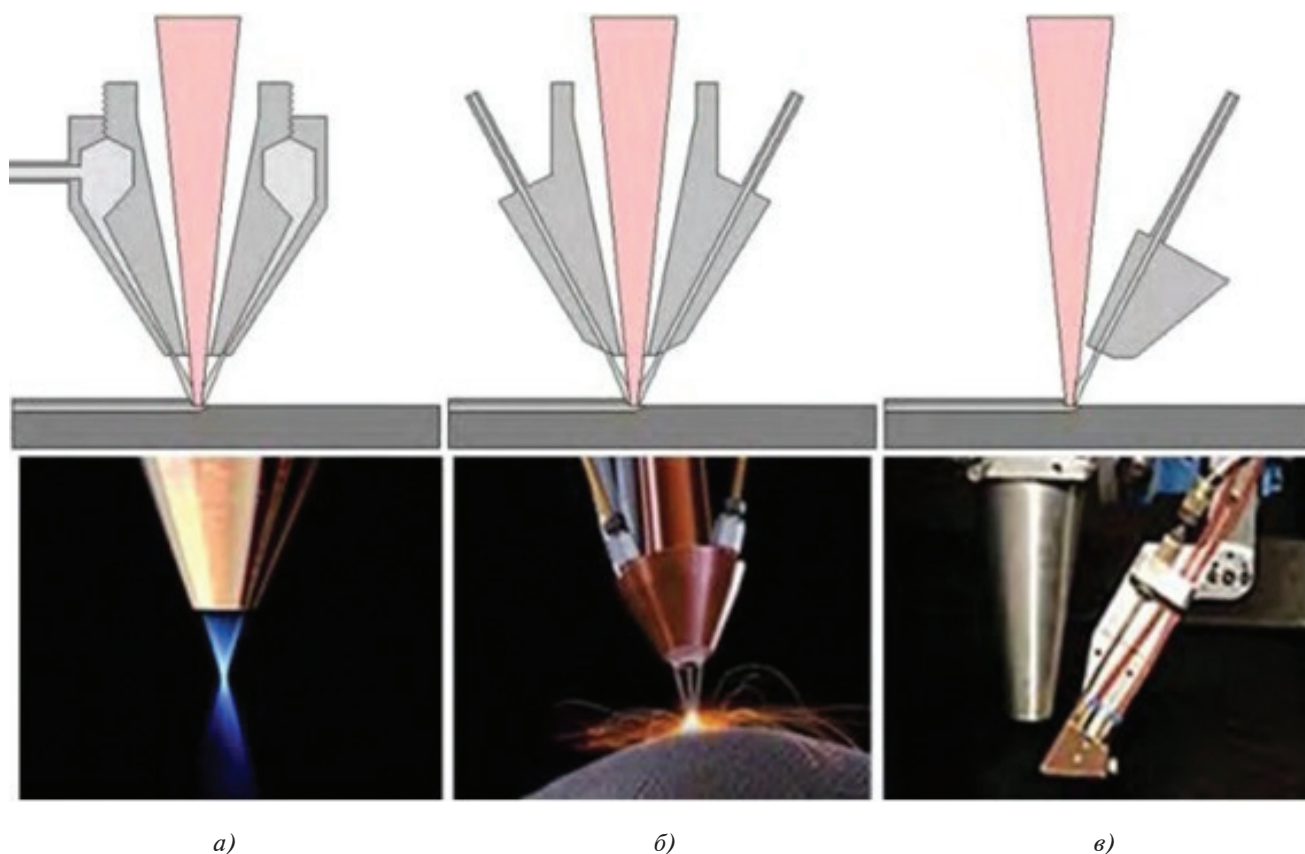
Сопло с коаксиальным кольцевым каналом (а), струйное коаксиальное сопло с несколькими потоками порошка (б) и сопло с боковой подачей порошка (в) [21, 27]
